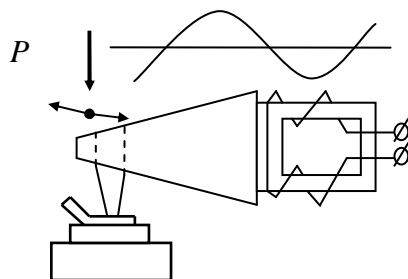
Схема ультразвуковой сварки с косвенным импульсным нагревом
